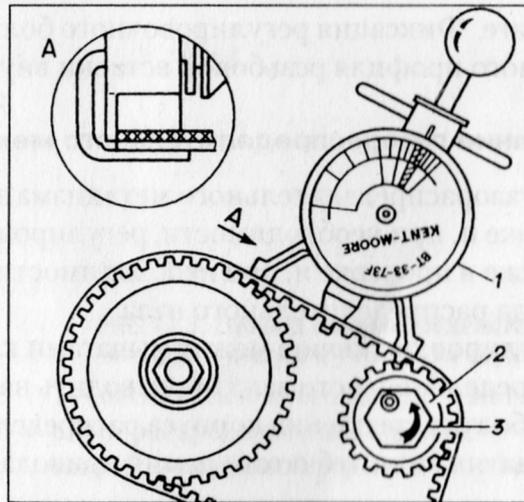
Проверка натяжения зубчатого ремня привода распределительного вала:
